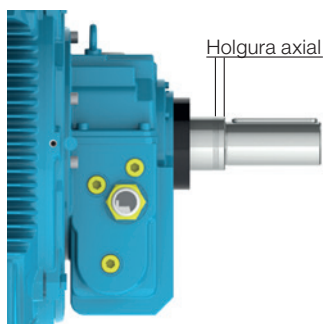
Holgura axial en motor equipado con cojinete de deslelevación
